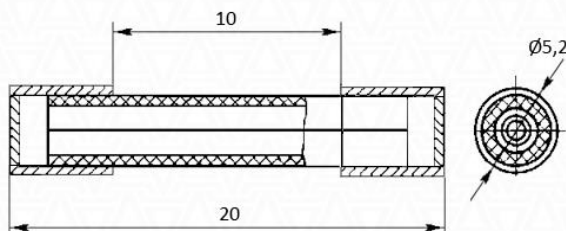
Габаритні розміри запобіжника ZH214-015
